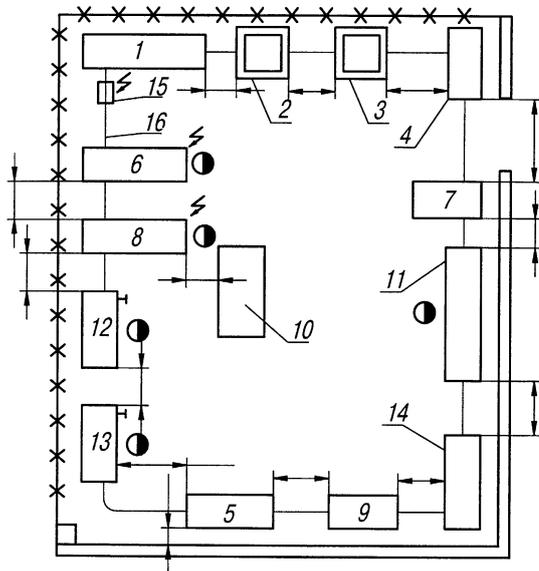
Примерная планировка сварочно-наплавочного участка
